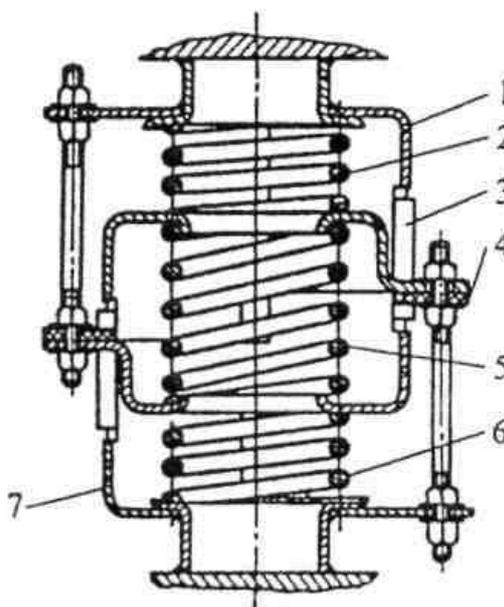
Виброизолятор металлический: 1- корпус; 2 - пружина; 3 - фрикционные планки; 4 - фрикционные накладки; 5, 6 - пружины; 7 – корпус
